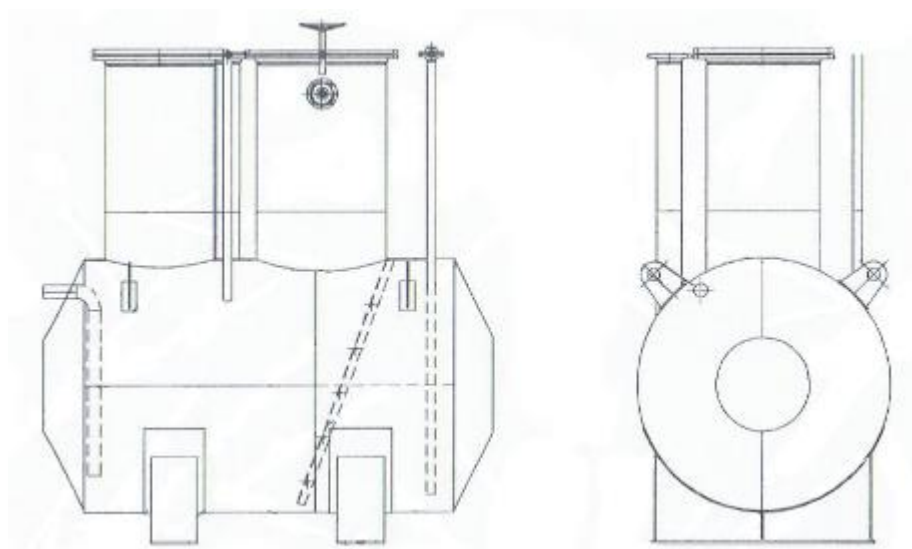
Эскиз общего вида резервуаров ЕП-5
